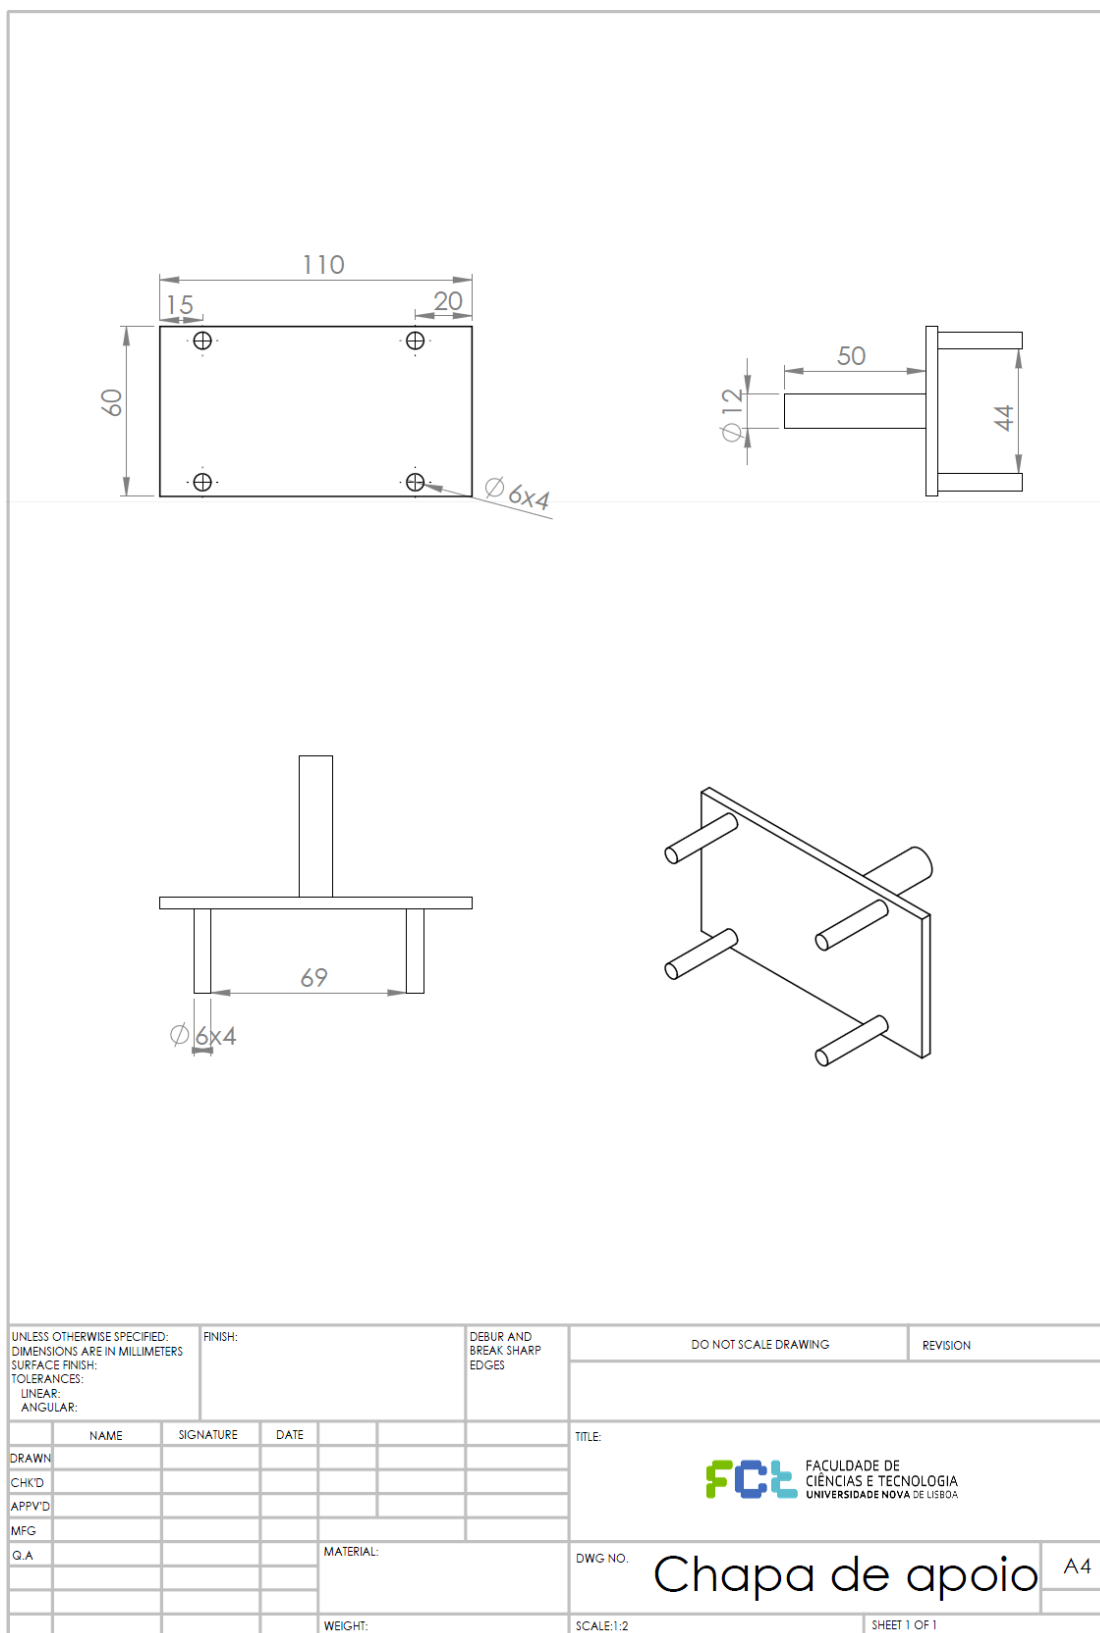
Desenho técnico da chapa de apoio da tocha de soldadura
